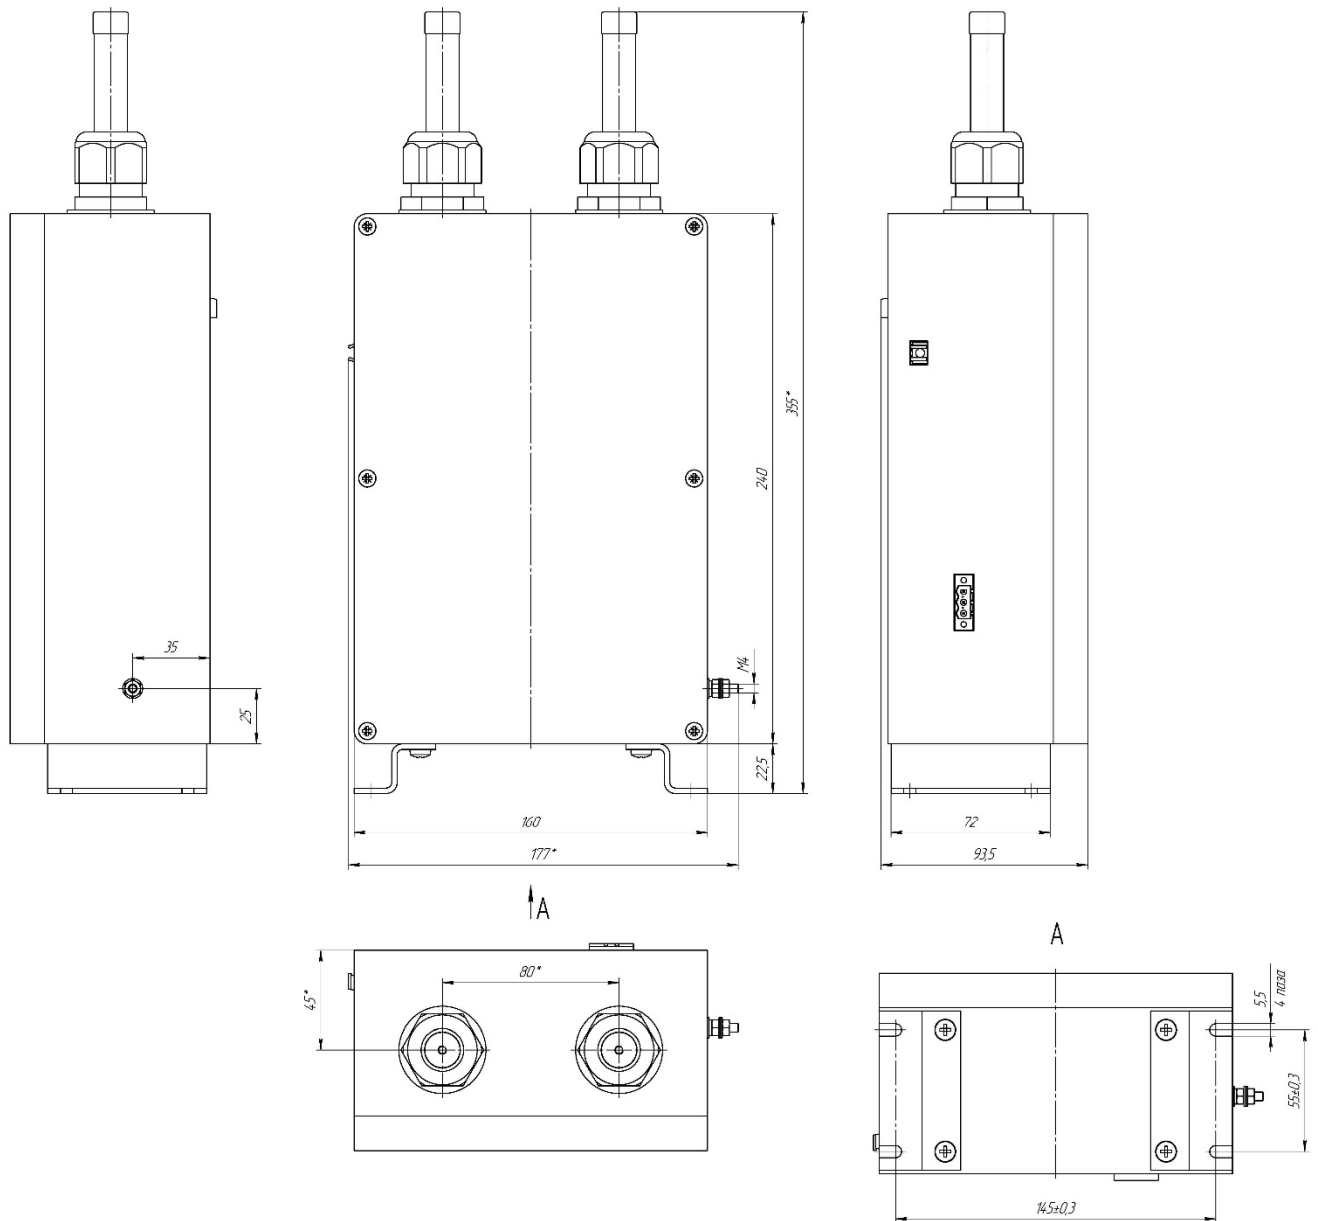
Габаритные и присоединительные размеры блока БКТН-ФПТ
